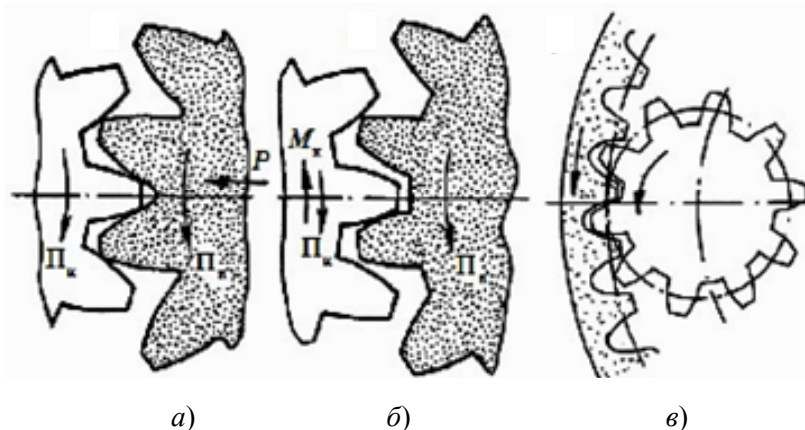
Схемы зубохонингования при различном зацеплении зубьев хона:
